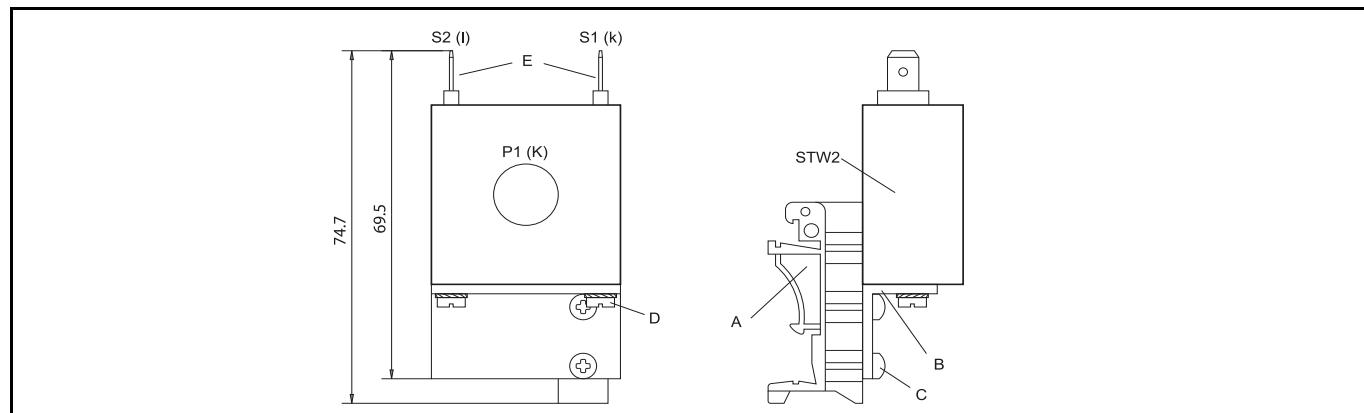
Variante de montaje 2 (todas las dimensiones en mm)
